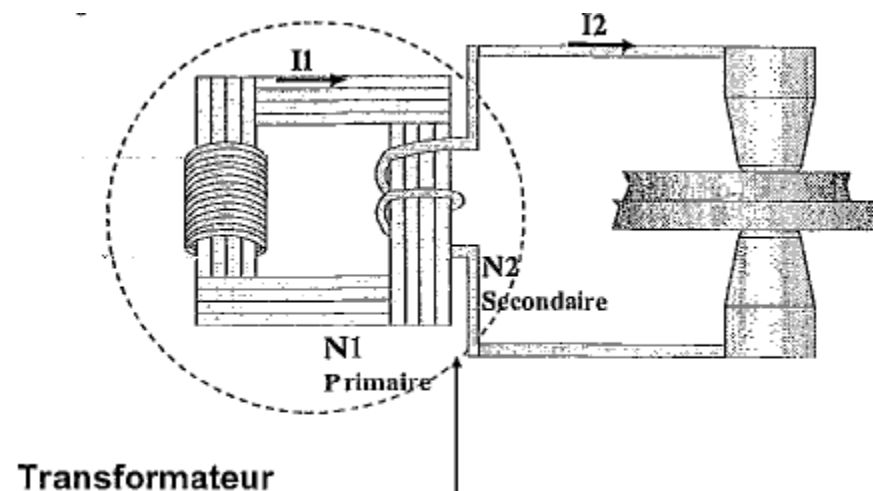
Transformateur de la machine de soudage par résistance
